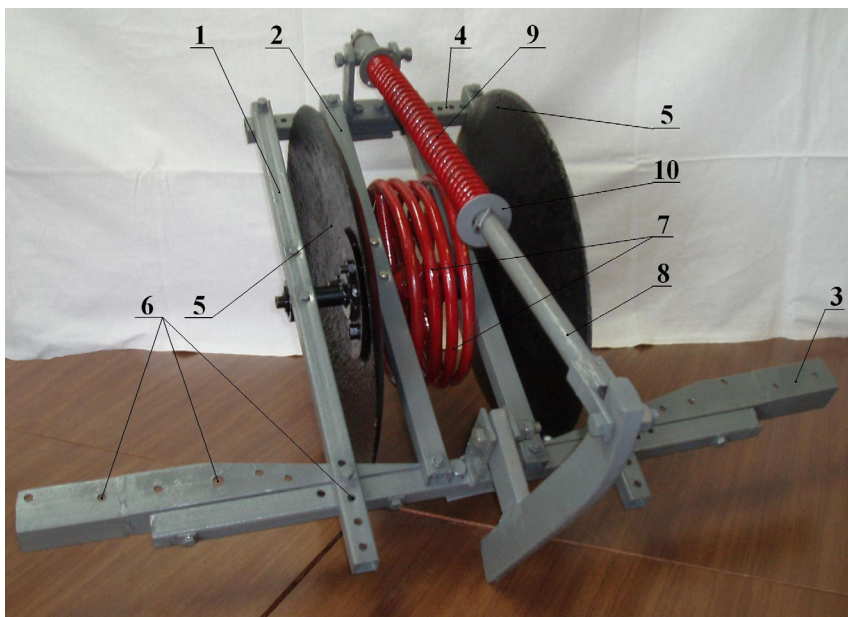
Каток: 1 – боковая балка; 2 – продольная балка; 3 – передняя балка; 4 – задняя балка; 5 – сферические диски; 6 – регулировочные отверстия; 7 – прикатывающие кольца; 8 – штанга; 9 – пружина; 10 – шайба
